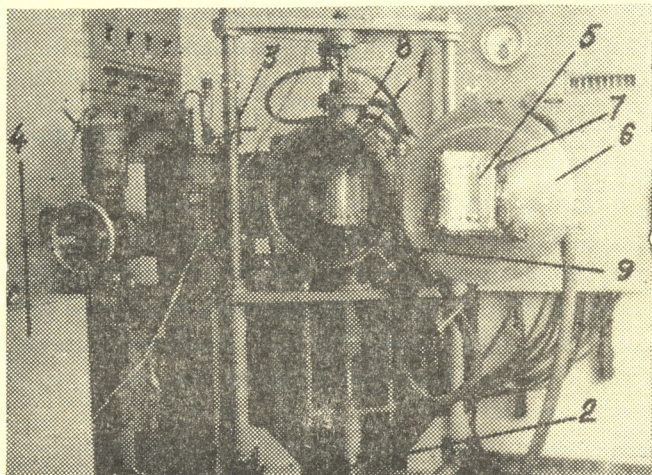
Установка диффузионной сварки УДС—431: 1 — сварочная камера, 2 — гидравлическая система, 3 — система откачки, 4 — блок питания и пульт управления, 5 — нагреватели, 6 — съёмные двери, 7 — тепловые экраны, 8 — верхний шток, 9 — нижний шток
